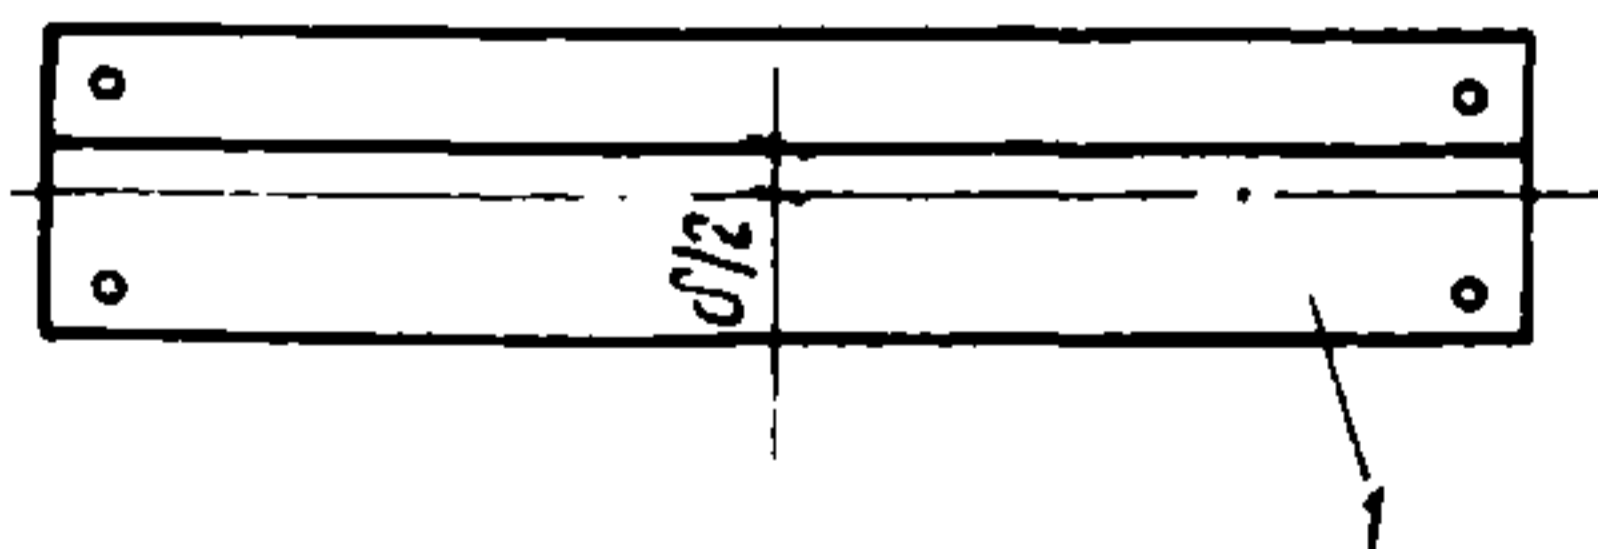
Разметка линии установки стенки стержня для настройки кондуктора
